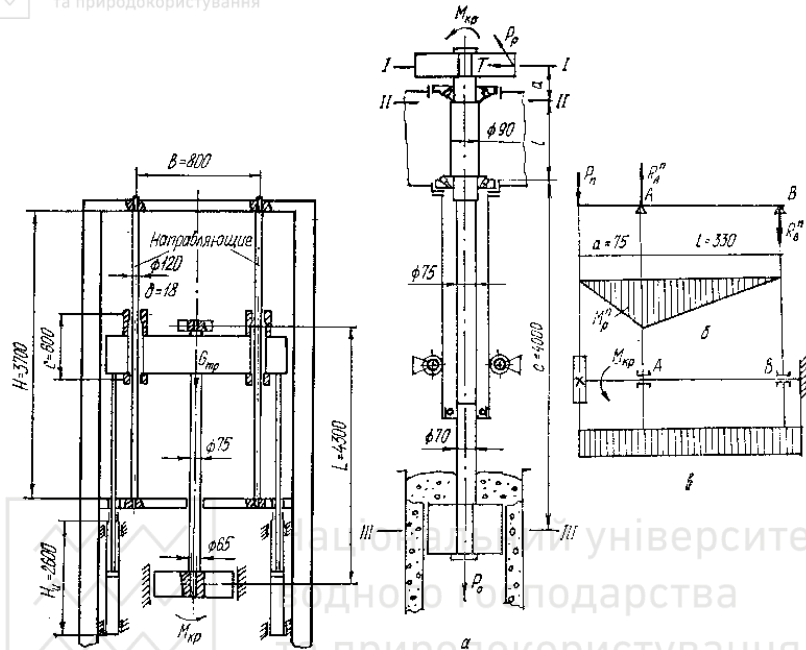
Розрахункова схема механізму обертання і підйому роликової головки
